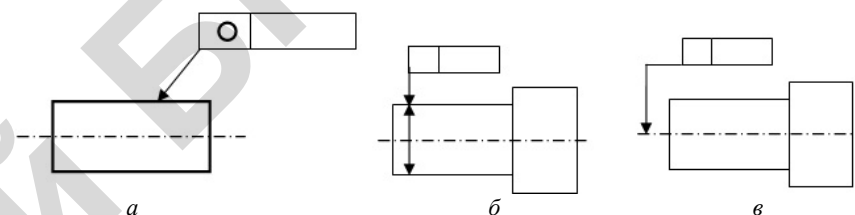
Рамки для обозначения допусков формы и расположения поверхностей на чертеже
